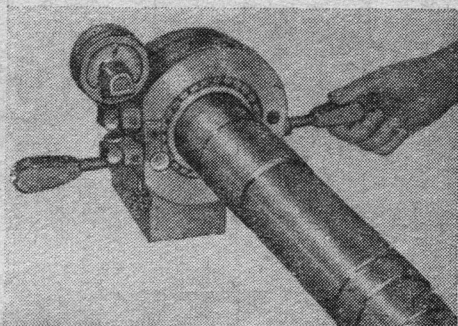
Регулирование радиального зазора в подшипнике с помощью прибора «Шведское кольцо»
